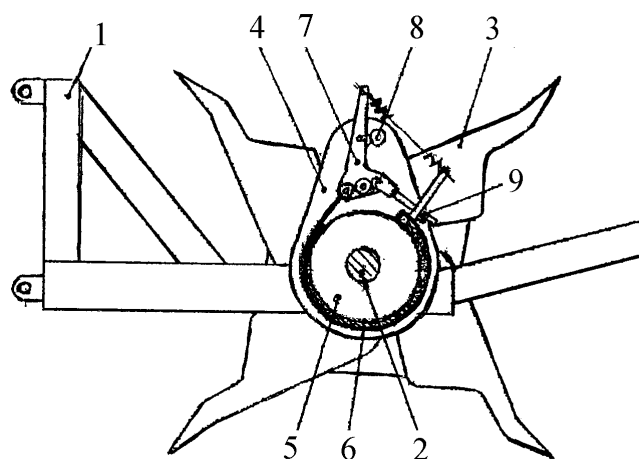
Орудие для подготовки микроповышений ОРМ-1,5: 1 – рама с навеской; 2 – вал; 3 – лопастной ротор; 4 – тормозной механизм; 5 – барабан; 6 – тормозная лента; 7 – рычаг; 8 – кулачок; 9 – механизм натяжения
